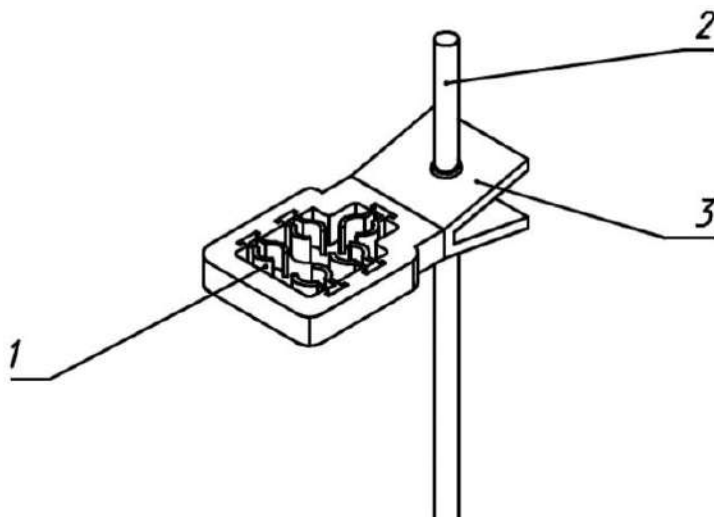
Внешний вид стойки штатива (2) с держателем (3) и зажимами (1)
